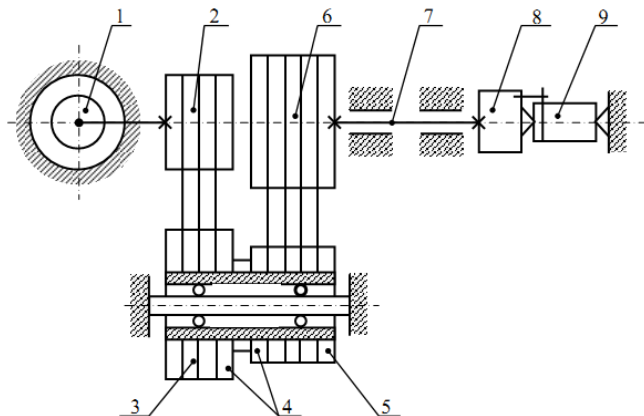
Схема приводу обертання заготовки верстата 3М151
